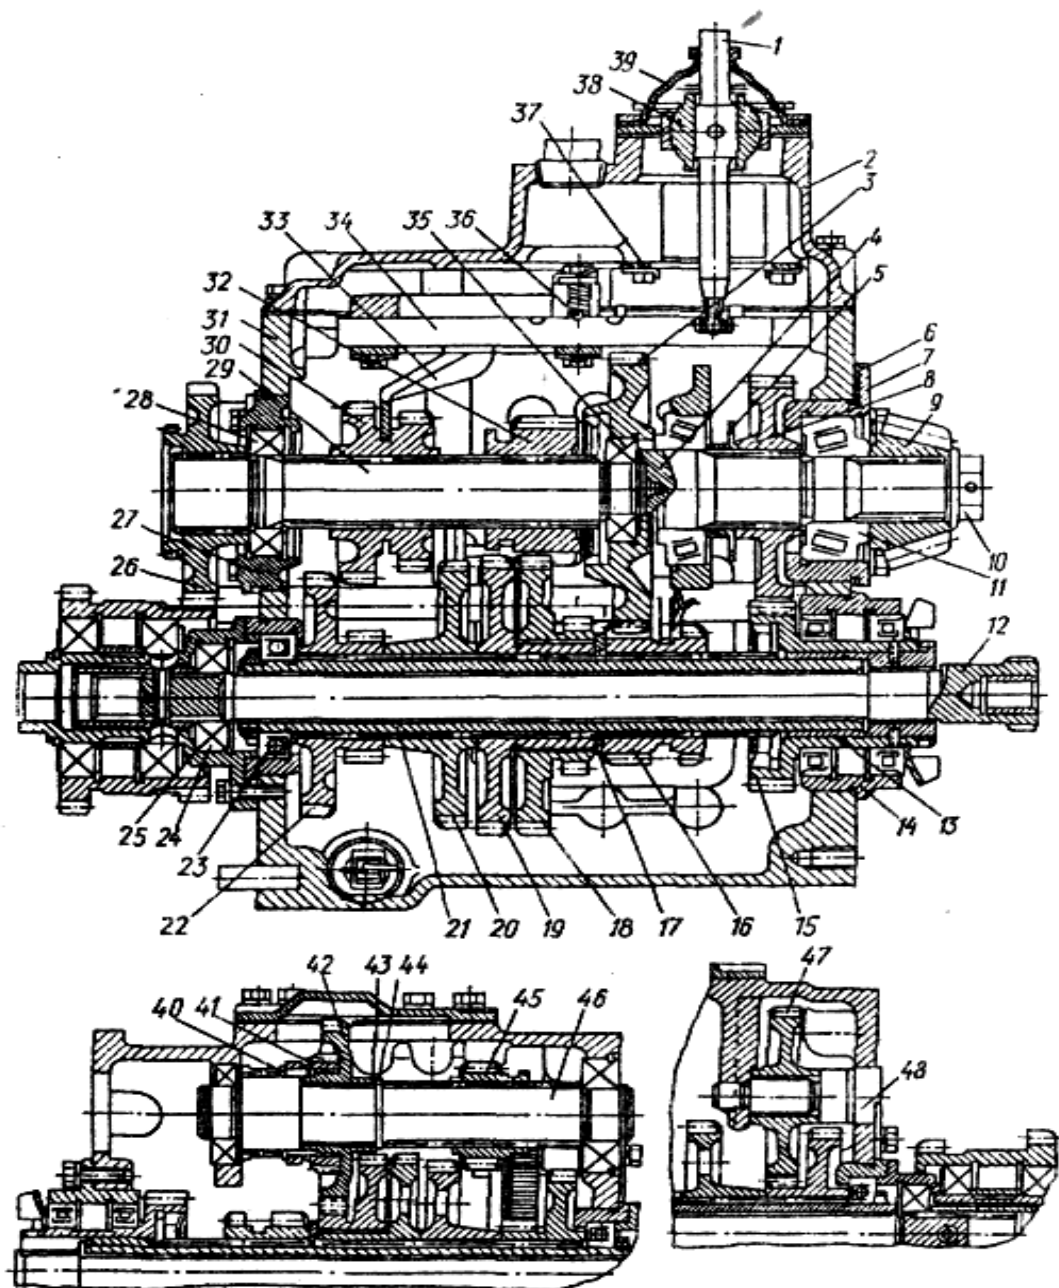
Коробки передач тракторів сімейства МТЗ із рухомими шестернями: 1 - важіль переключення передач; 2 - кришка; 3 - ведена шестерня першої ступіні редуктора; 4 - вторинний вал; 5 - пластинчаста пружина; 6 - регульовальні прокладки; 7, 14, 25 і 27 - стакани; 8 - ведена шестерня другої ступені редуктора; 9 - ведуча шестерня головної передачі; 10 - гайка; 11 - конічні роликові підшипники; 12 - вал приводу ВОМ; 13 - втулка; 15 - ведуча шестерня другої ступені редуктора; 16 - ведуча шестерня першої ступені редуктора; 17 - кільце; 18 - проміжна шестерня; 19 і 20 - ведені шестерні третьої і четвертої передачі; 21 - проміжний вал; 22 - ведена шестерня п'ятої передачі і
